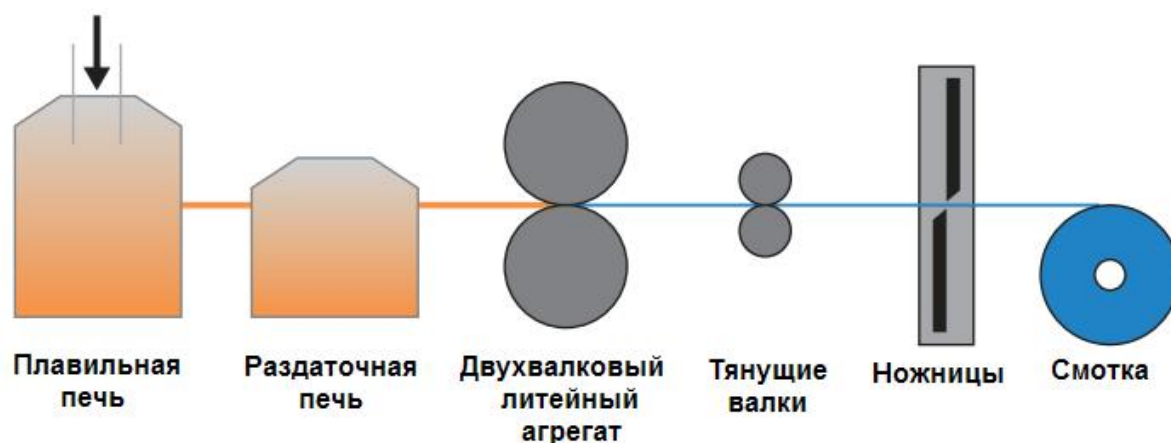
Двухвалковый литейный агрегат для производства алюминиевой полосы
